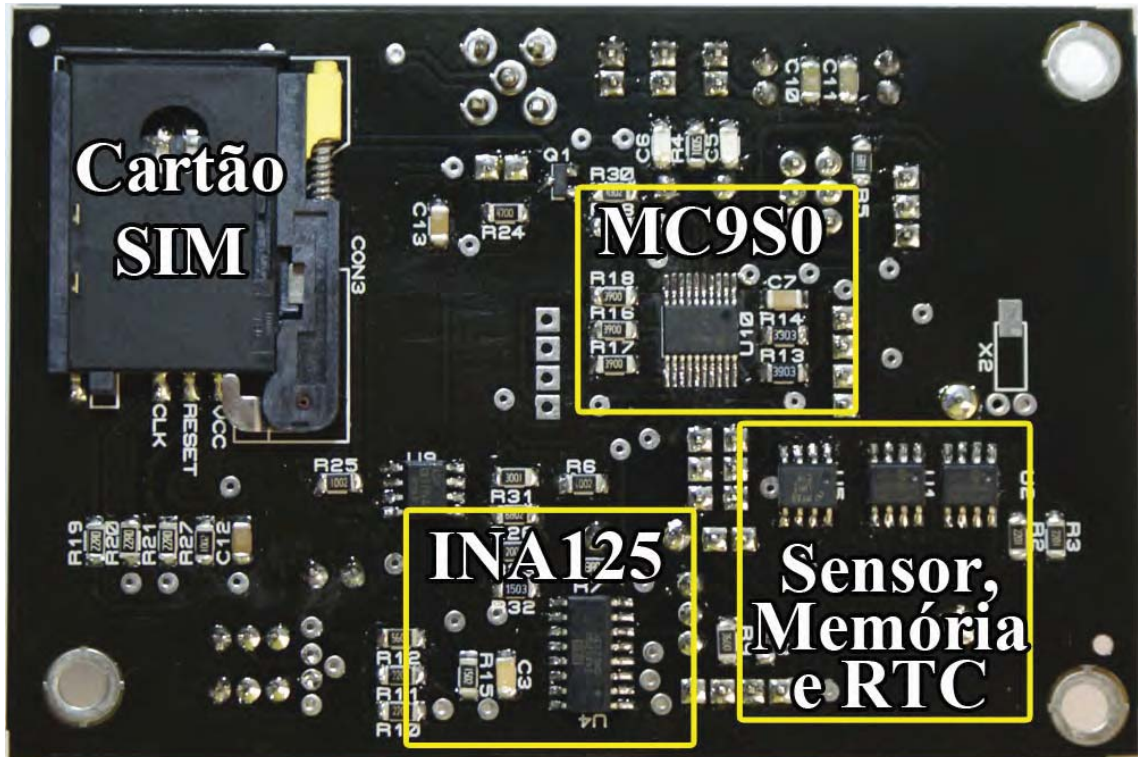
PCB - Lado da Solda. Foto: o autor.
